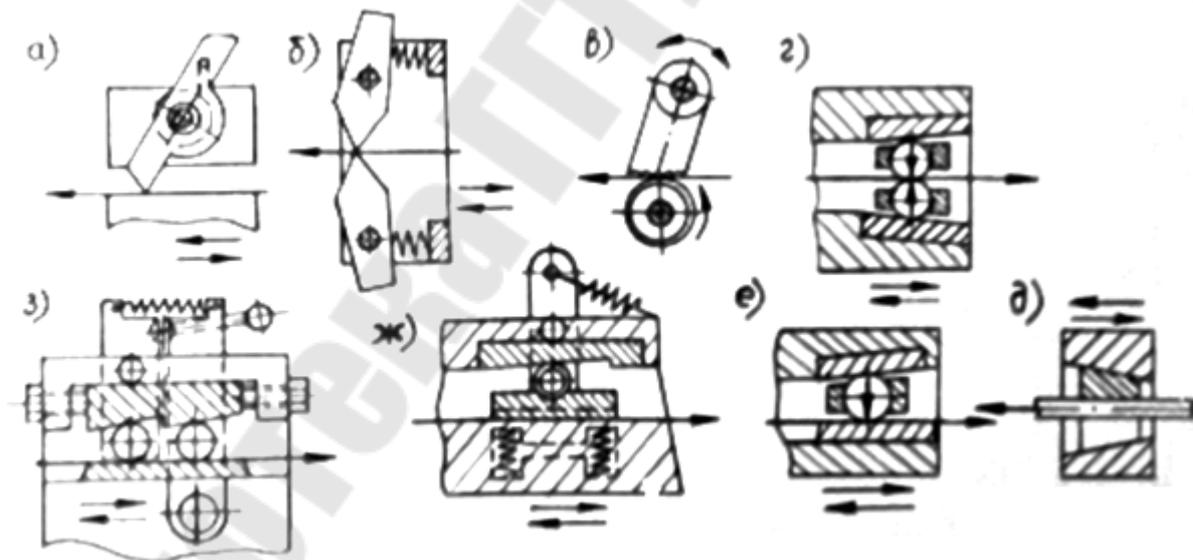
Схемы клиновых и ножевых захватных органов: а,б – при помощи ножа, в - при помощи кулачка, г - роликовые, д - цанговые; е - при помощи одного ролика; ж - применение промежуточной пластины; з - клиновые обоймы
